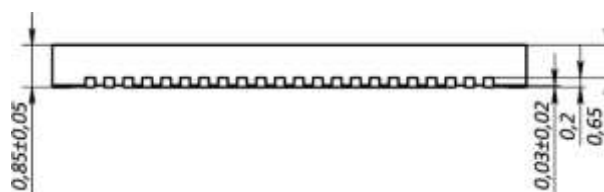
Габаритные размеры корпуса микроконтроллера (вид сбоку)
